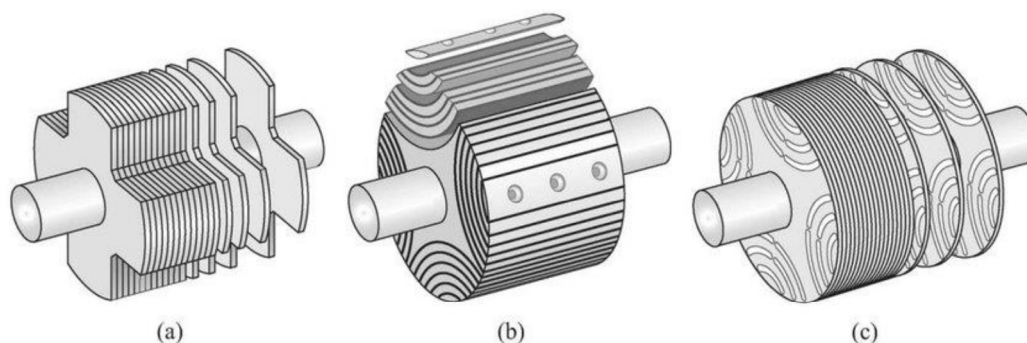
Tipos de rotor do MSR. (a) rotor de pólos salientes simples; (b) rotor laminado axialmente; (c) rotor laminado transversalmente [9].
